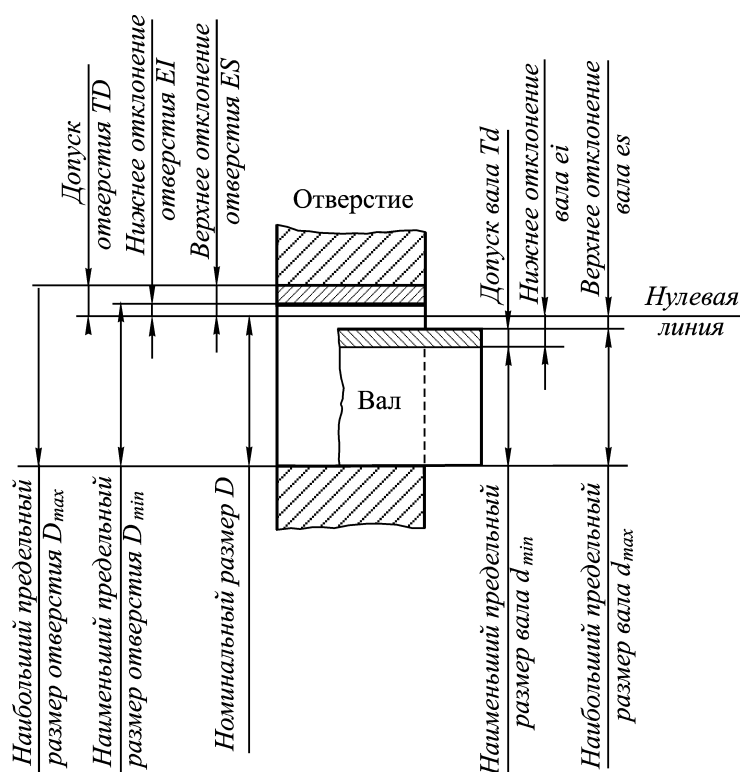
Номинальный размер, предельные размеры, предельные отклонения и допуски для отверстия и вала в посадке с зазором
